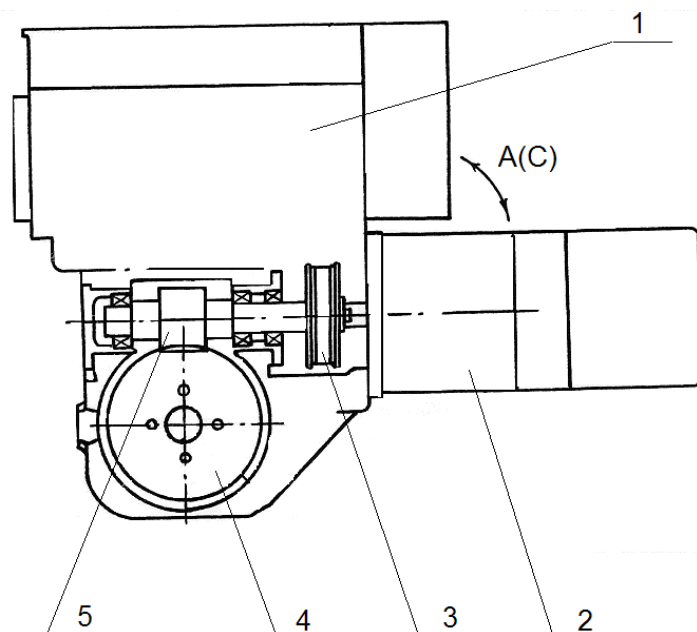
Механизм поворота руки манипулятора (движение A/C).
